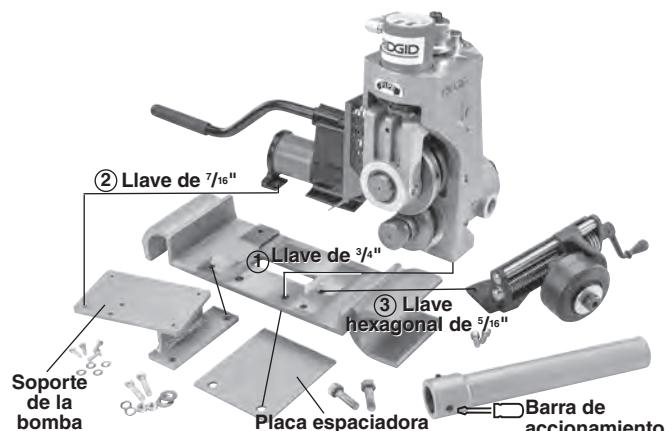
Montaje de la ranuradora 918 sobre la base de la roscadora 1224
